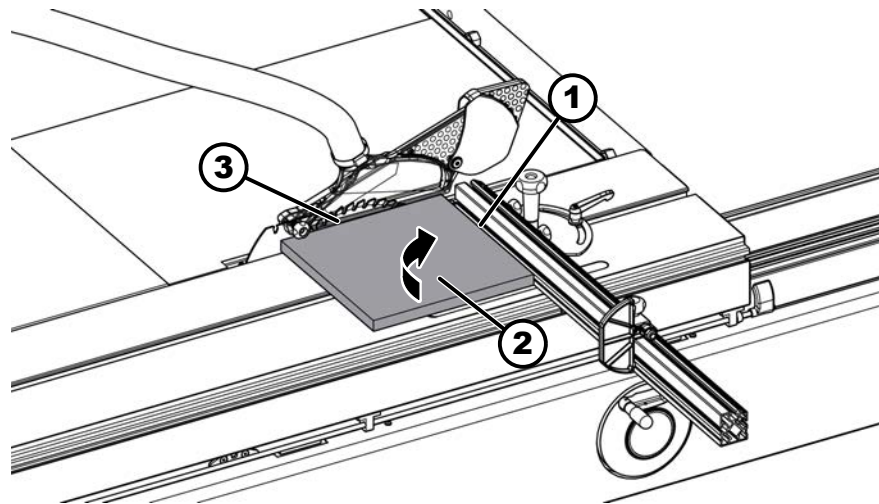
Probeschnitt - Winkel Ablänganschlag
